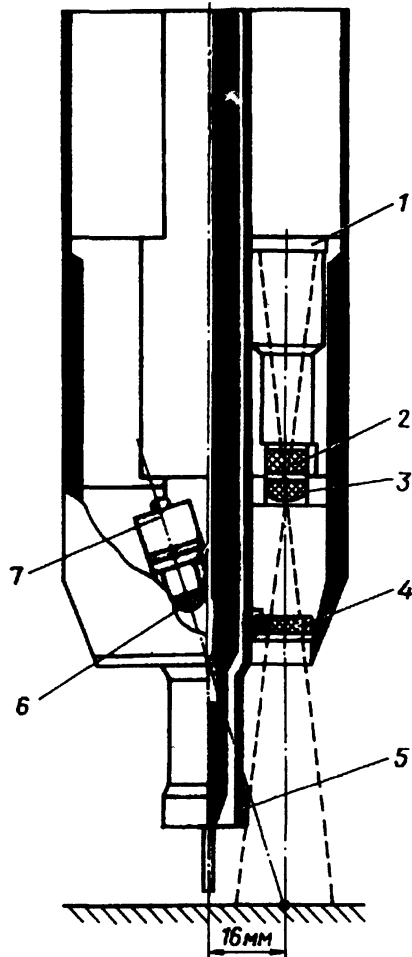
Схема видеосенсора, расположенного в одном корпусе со сварочной горелкой: 1 — фотоприемник (ПЗС-матрица); 2 — интерференционный фильтр; 3 — объектив; 4 — окно; 5 — газовое сопло горелки; 6 — цилиндрическая оптика; 7 — лазерный осветитель
